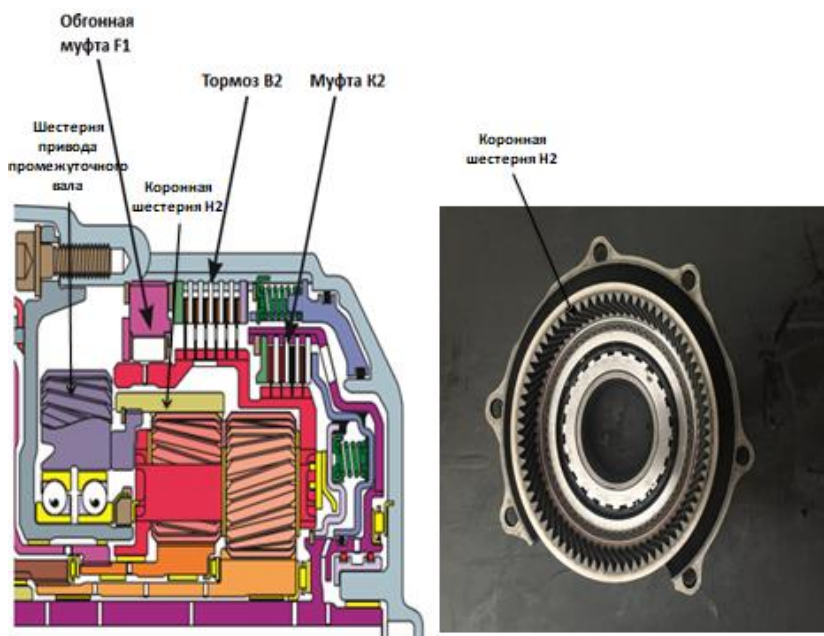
Устройство коронной шестерни и ее расположение в картере
